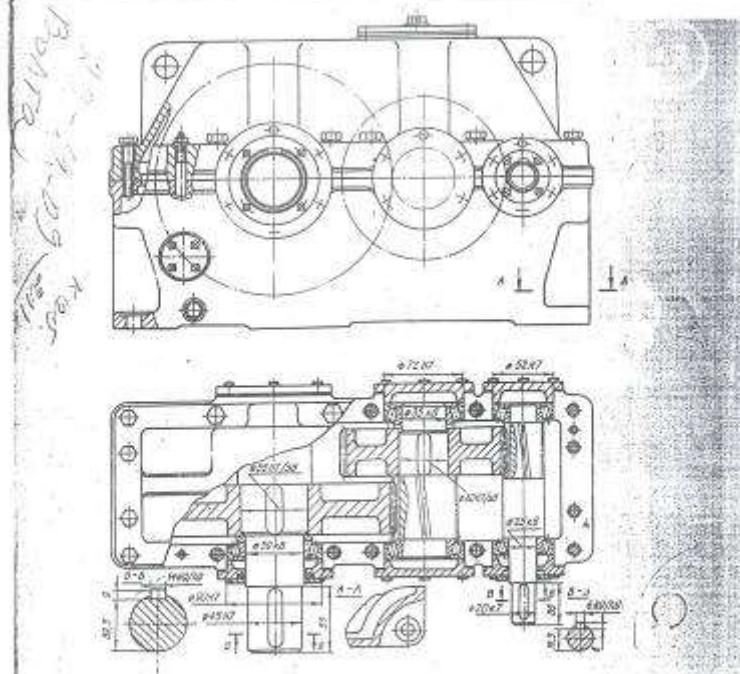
Двухступенчатый цилиндрический редуктор
